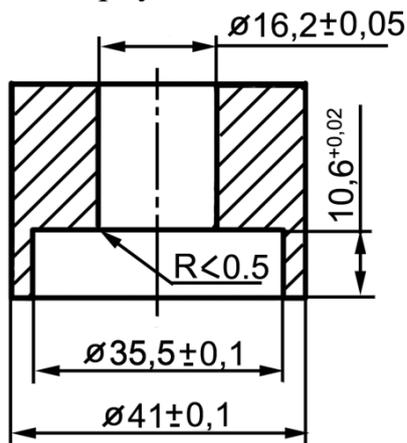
Оправка для запрессовки уплотнения водяного насоса (Основные конструктивные размеры)
